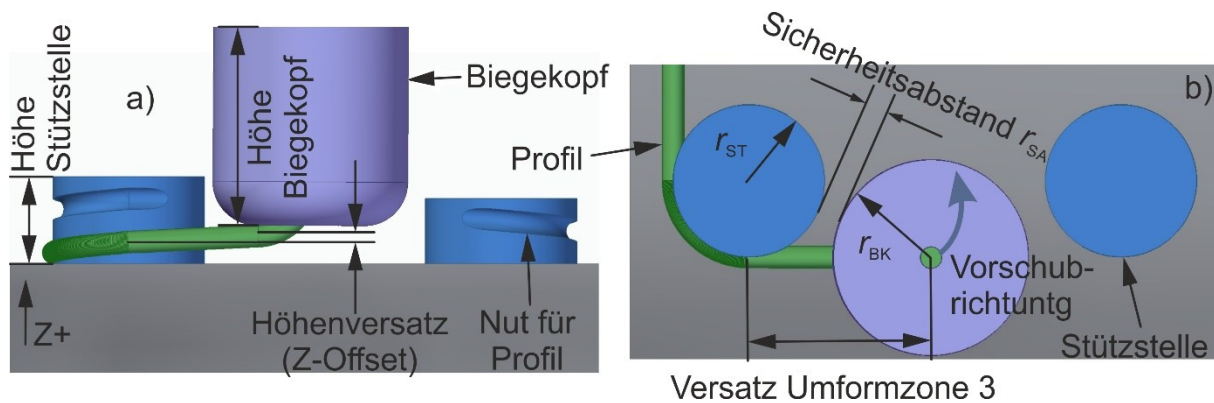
3D-Umformen Prinzipskizze: a) Seitenansicht, b) Draufsicht
